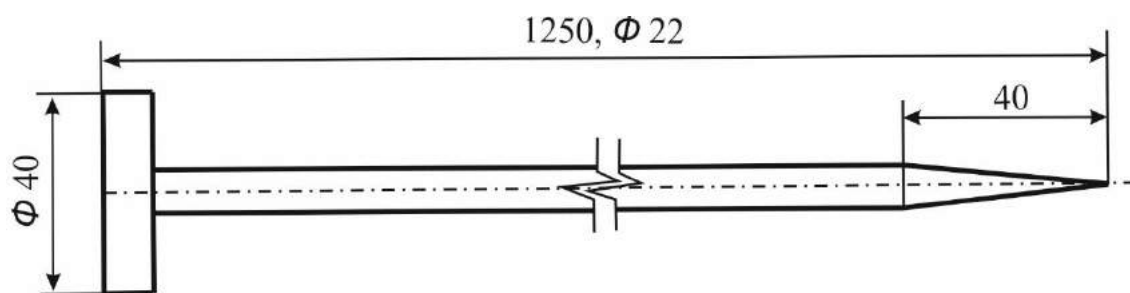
Внешний вид забивного анкера принятого типоразмера
